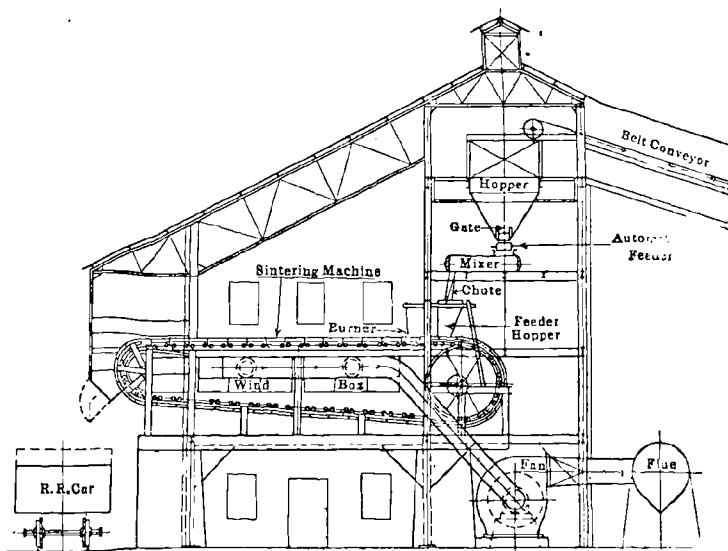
Table horizontale d'agglomération de la Dwight & Lloyd Sintering C°
